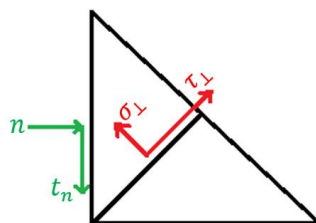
Tensiones en plano de la garganta y en plano abatido
